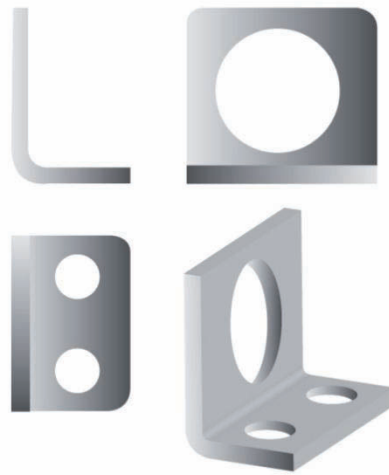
Diseño CAD acoplamiento del pistón A.
